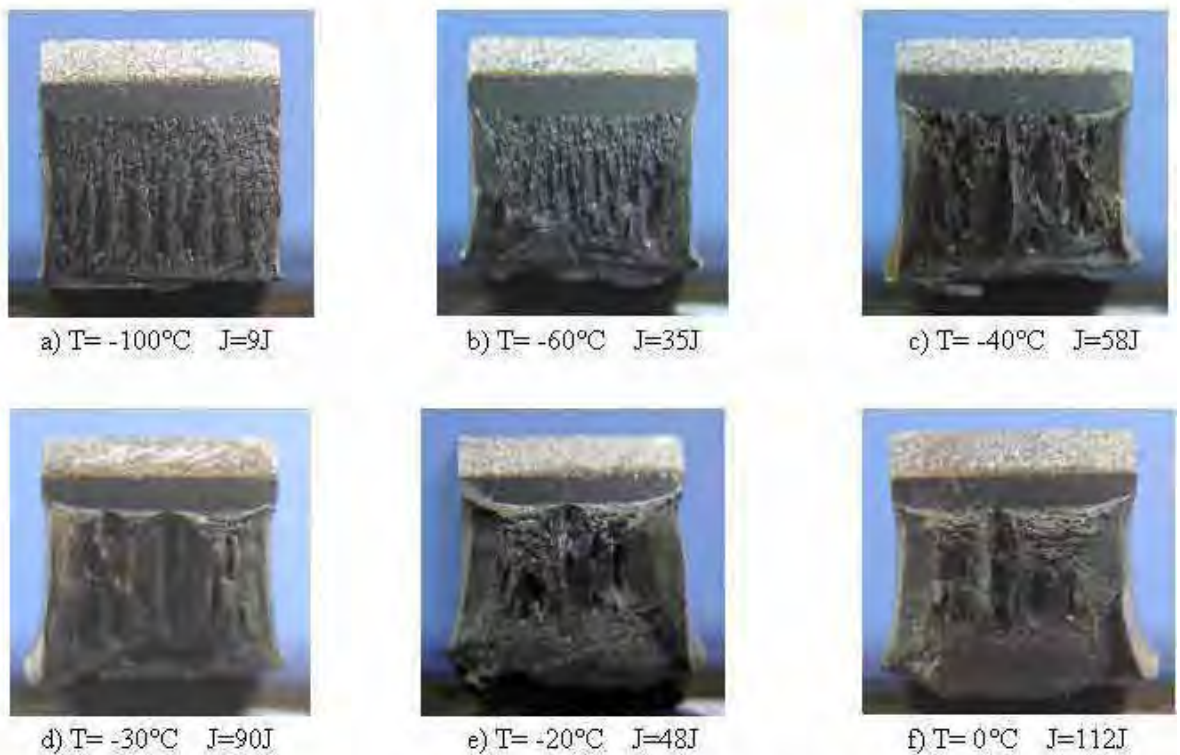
Fractografia da superfície de fratura do aço API - CF, corpo-de-prova pré-trincado.
